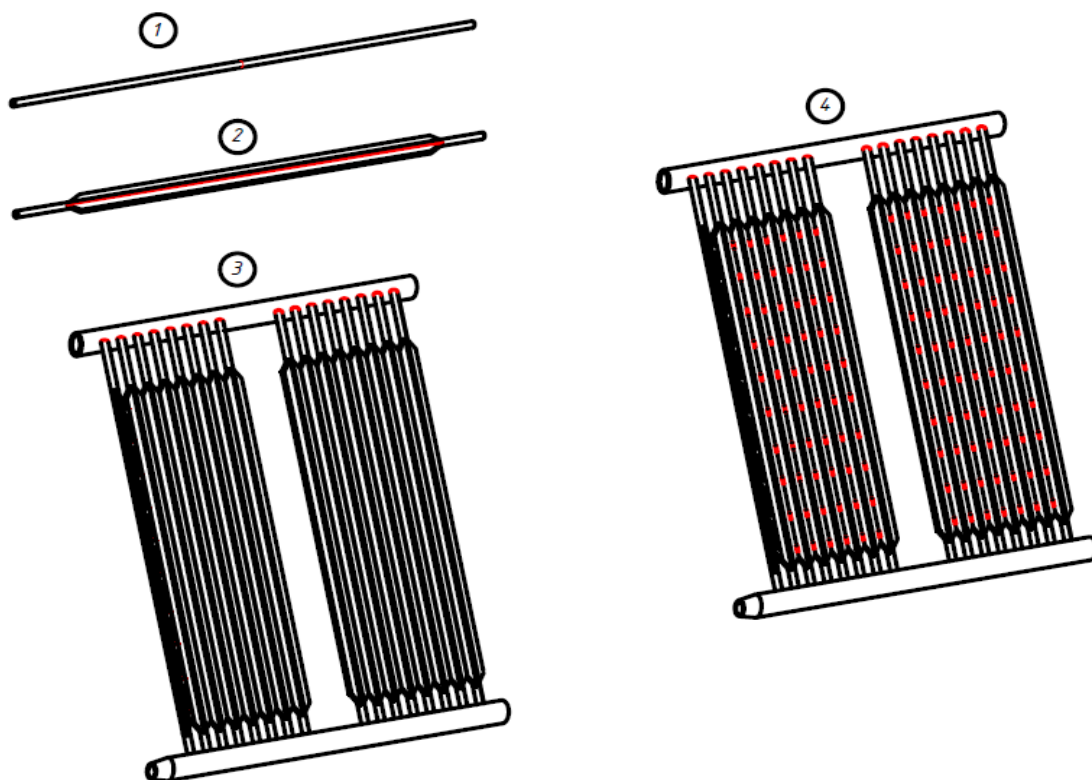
Технология сборки и сварки ширмы водяного экономайзера
